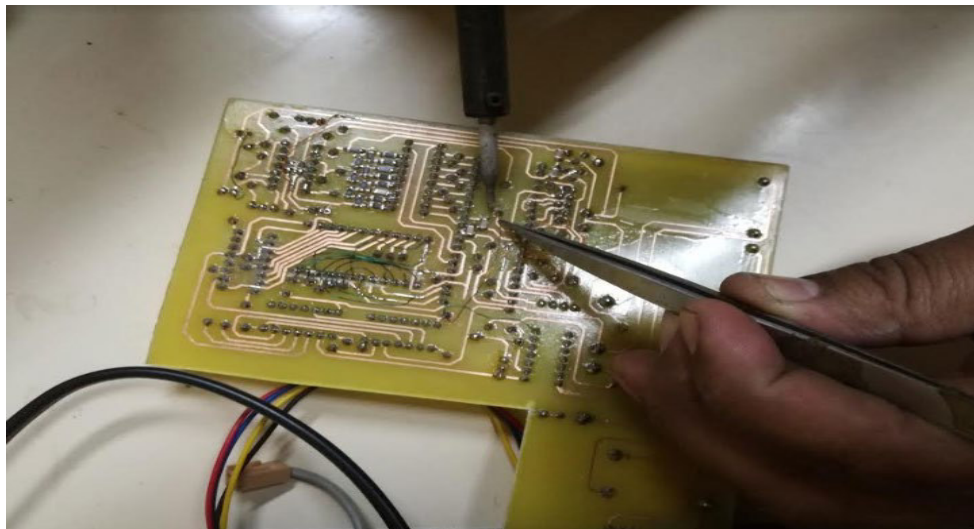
Soldadura de los componentes electrónicos para el acabo final de la tarjeta electrónica.
